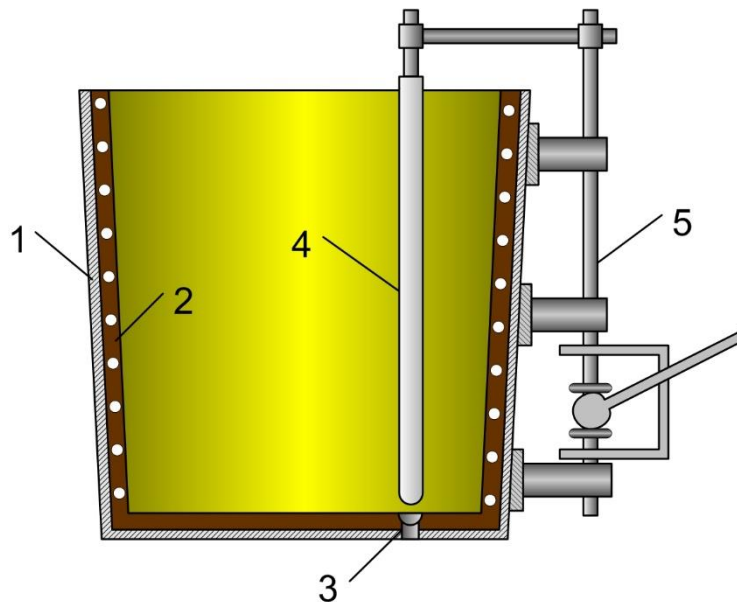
Модель розливного ковша: 1 – металевий кожух; 2 – внутрішня стінка ковша зі спіралями нагрівача; 3 – розливний стакан; 4 – стопор; 5 – стопорний механізм.
